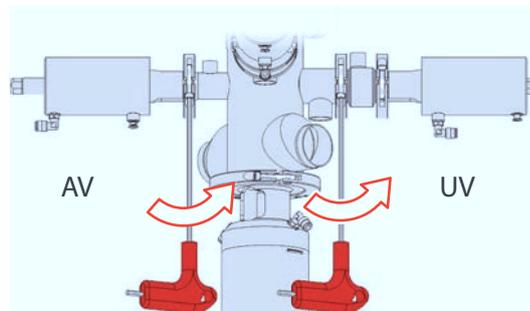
Débloquer la vis du collier de serrage de la vanne latérale
